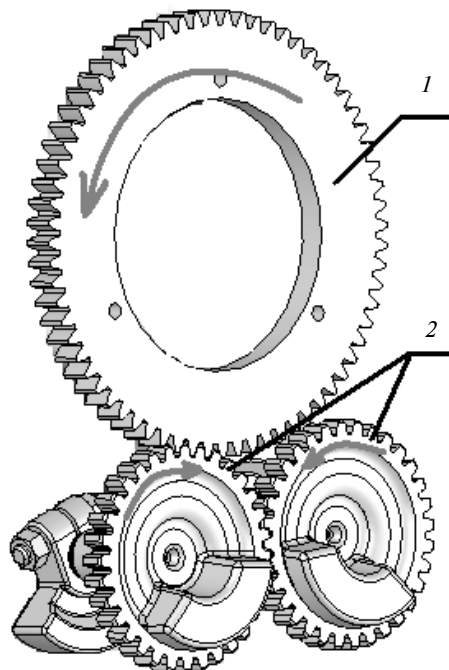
Схема привода вала уравнивающего механизма со специальной шестерней привода
